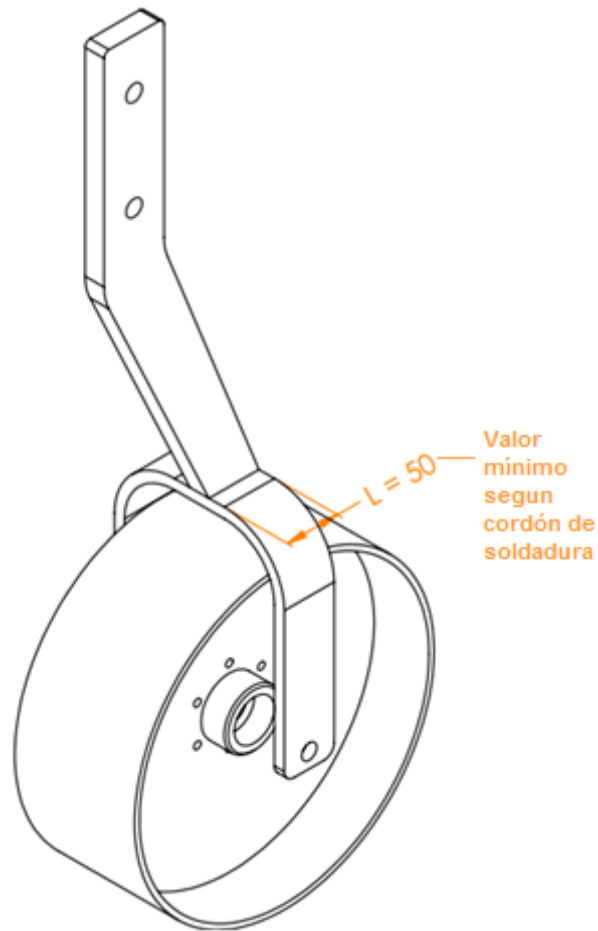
cordón de soldadura mínimo en unión brazo soporte - horquilla. Elaboración propia.
